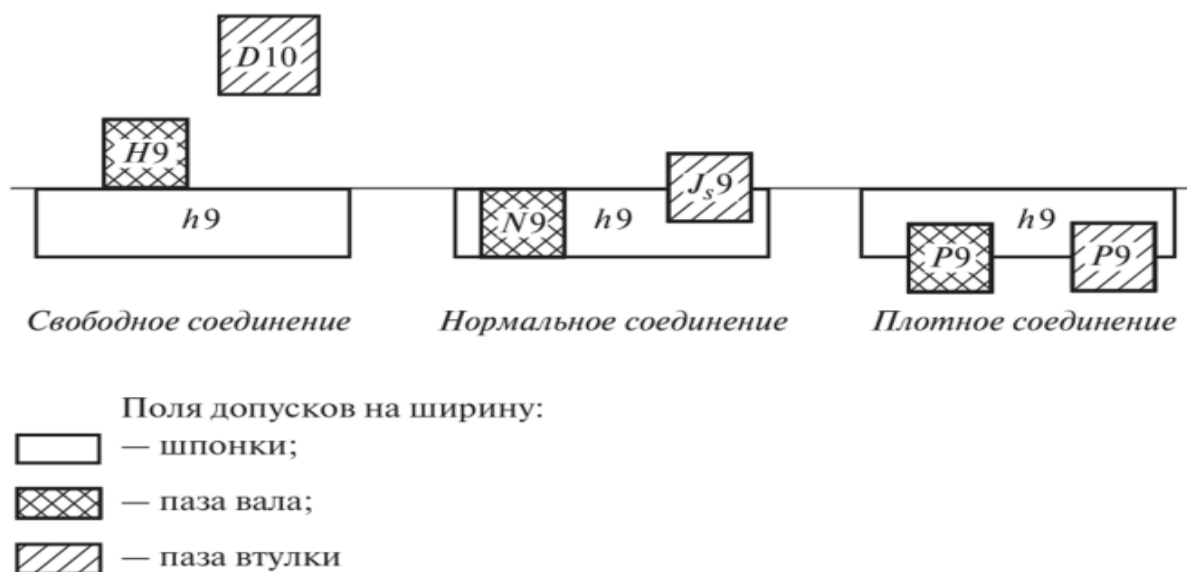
Поля допусков шпоночного соединения
